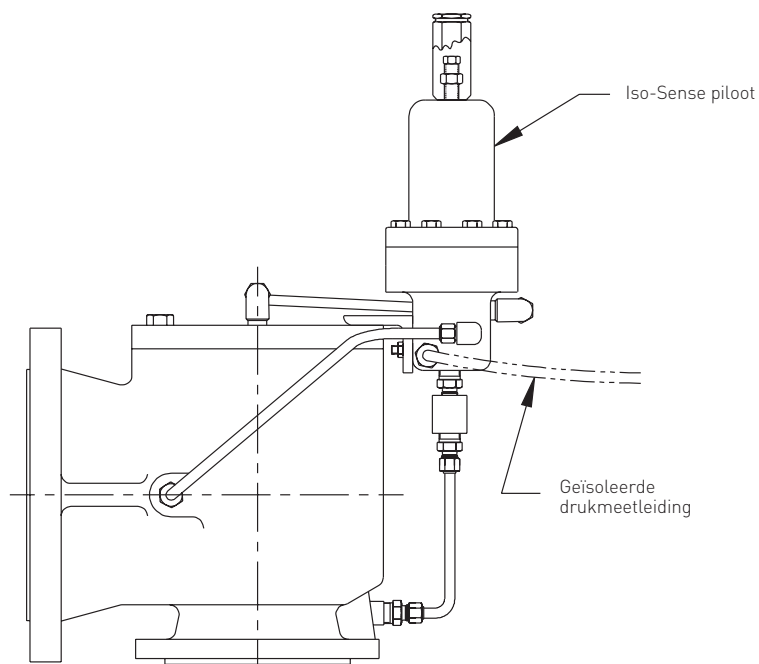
TESTOPSTELLING VOOR AFSLUITER MET PILOOT MET MEETLEIDING
